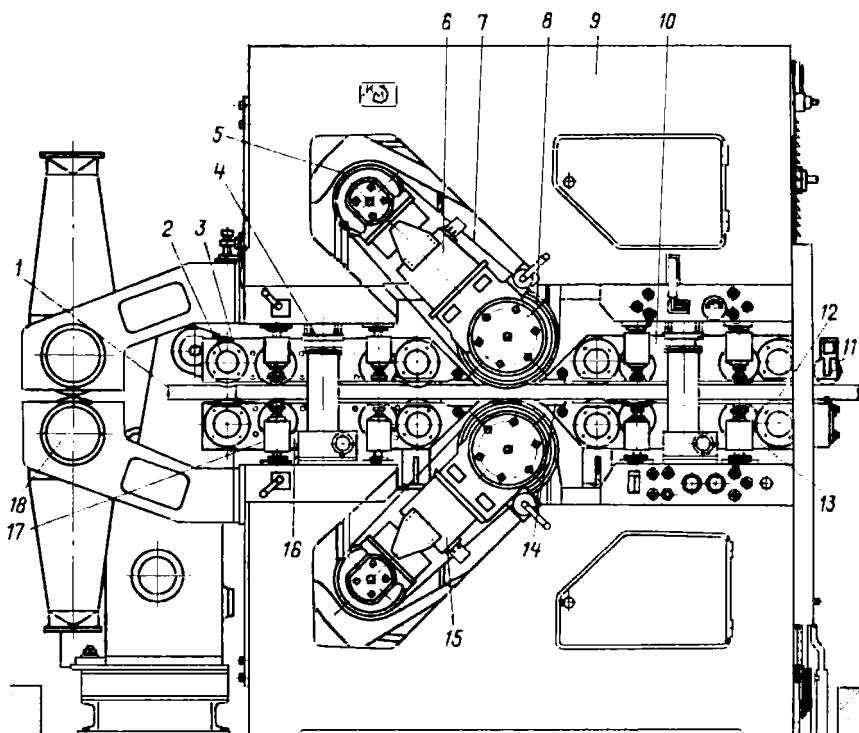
Схема калибровально-шлифовального станка ДКШ-1:
